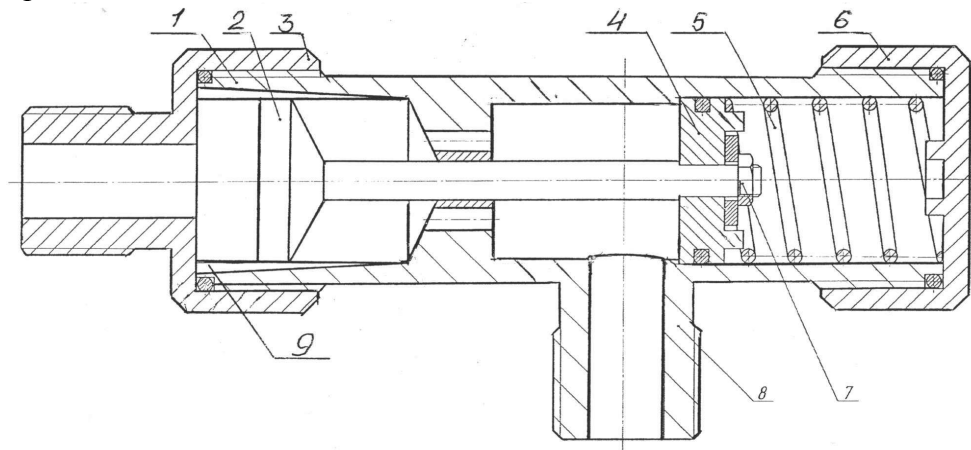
Запорно-регулирующее устройство: 1- корпус; 2 – клапан; 3 – крышка со штуцером; 4 – втулка; 5 – пружина; 6 – крышка; 7 – гайка с шайбой; 8 – штуцер; 9 – дроссельные каналы
